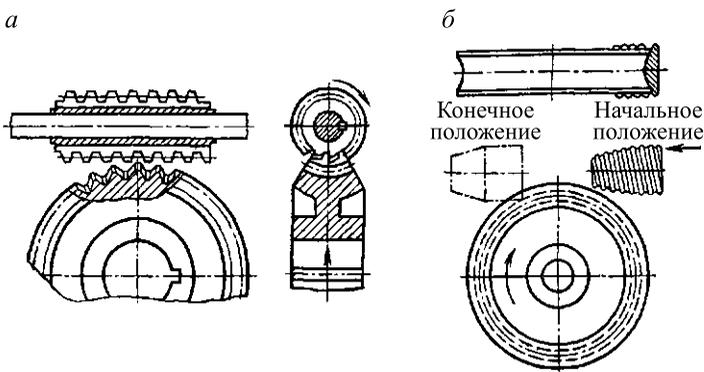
Схемы зубонарезания червячных зубчатых колес червячными фрезами
